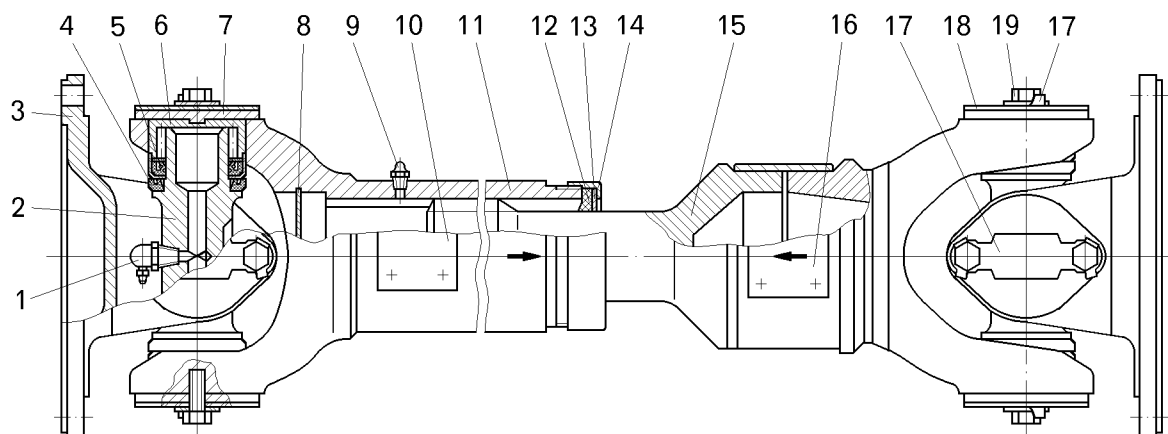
Карданный вал гидромеханической передачи:
